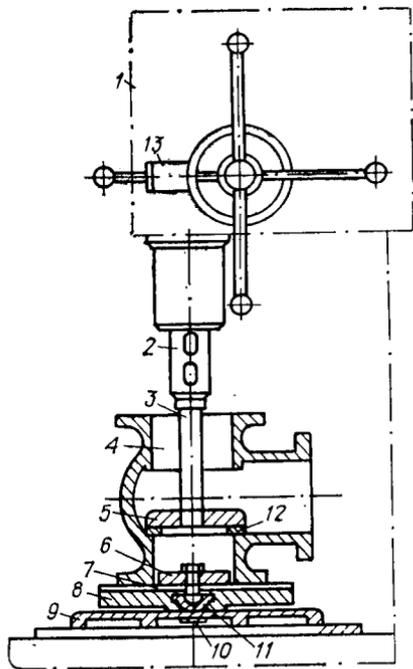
Приспособление для притирки уплотнительной поверхности корпуса задвижки на сверлильном станке:
